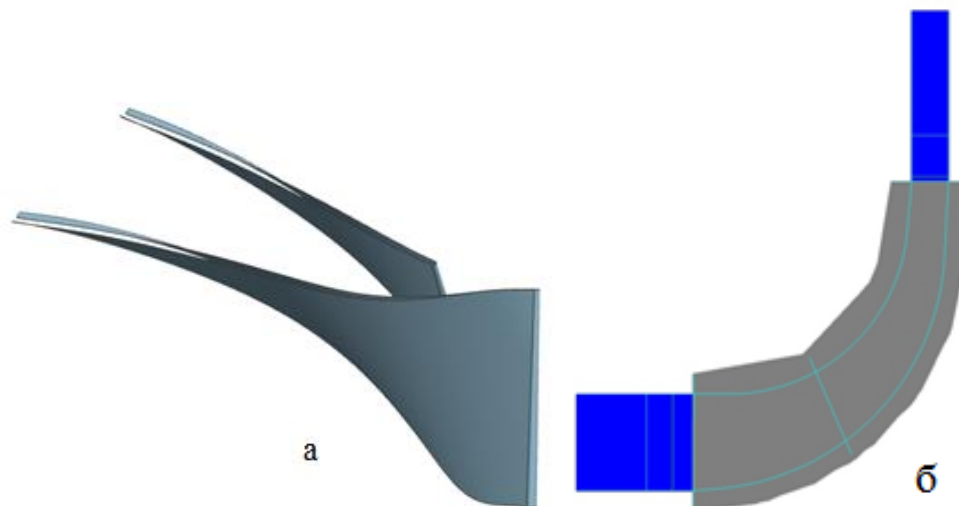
Поверхности лопаток (а) и контур меридионального сечения (б) рабочего колеса центробежного компрессора
